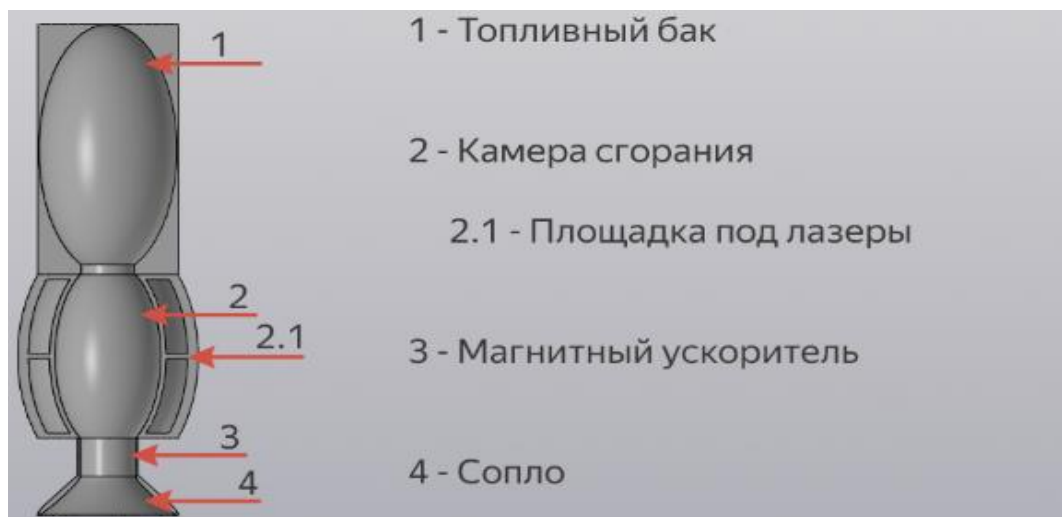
Схема 3D-модель плазменного ракетного двигателя
